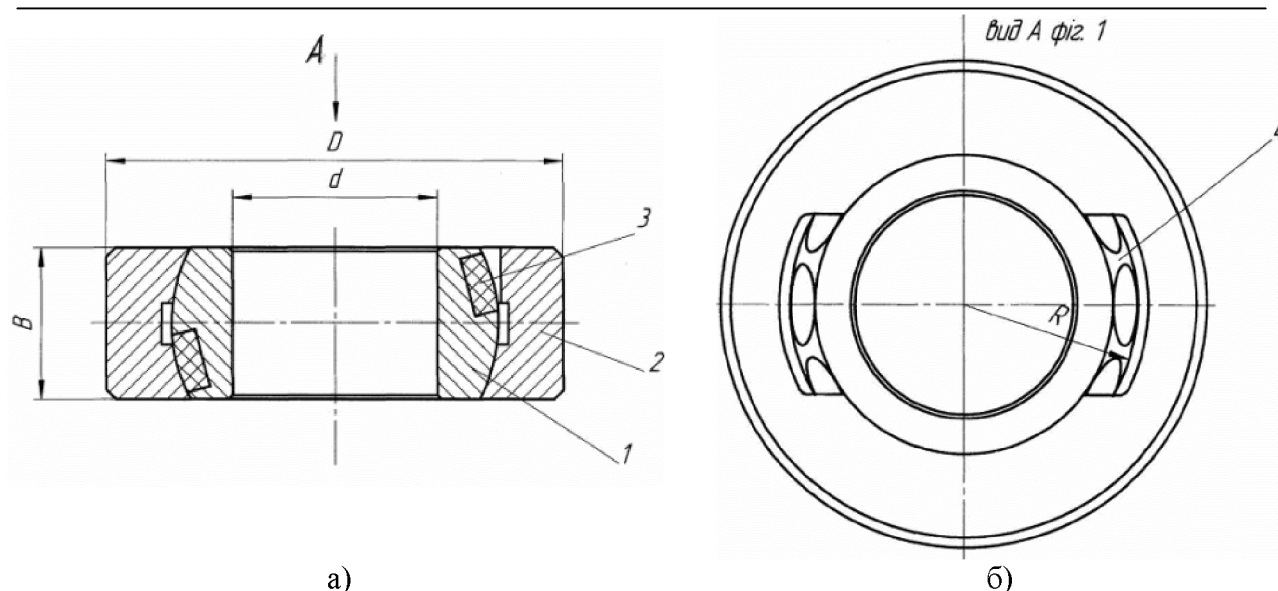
Сферичний самомастильний підшипник за пат. 44497: розріз (а) та загальний вид (б)
